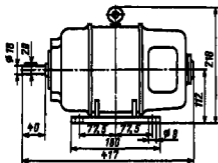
21 Габаритные и установочные размеры двигателя ПБ-12С
